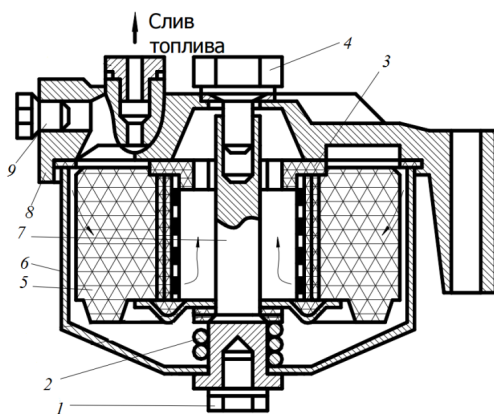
Фильтр тонкой очистки топлива: 1 – пробка; 2 – пружина; 3 – вставка; 4 – болт; 5 – фильтрующий элемент; 6 – корпус; 7 – центральный стержень; 8 – крышка; 9 – пробка для удаления воздуха
